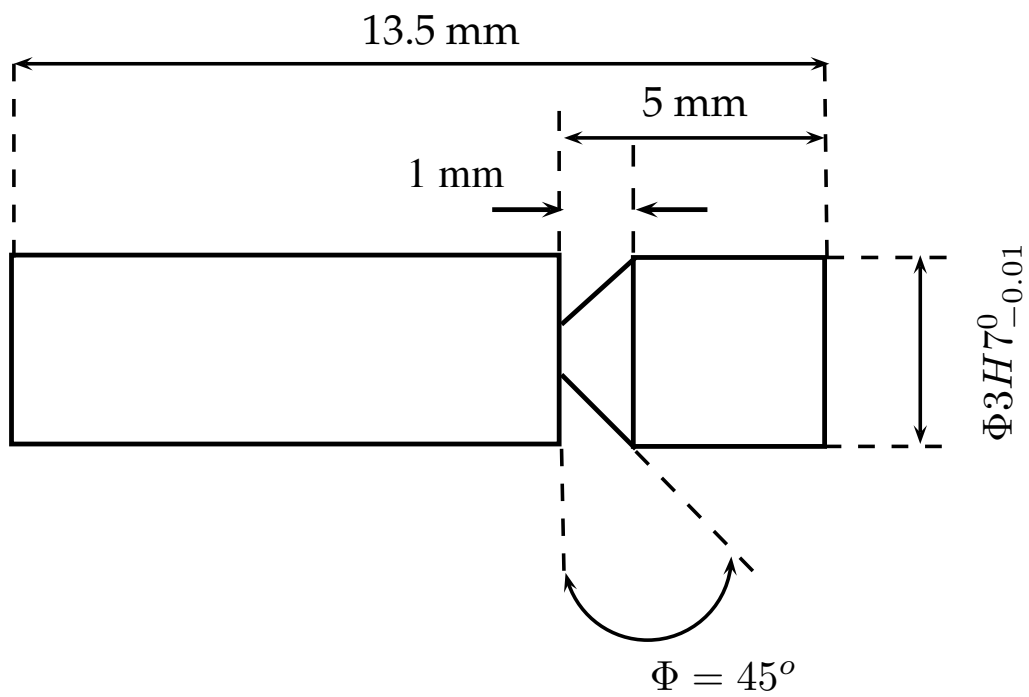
Plan utilisé pour fabriquer les éprouvettes Auger.
